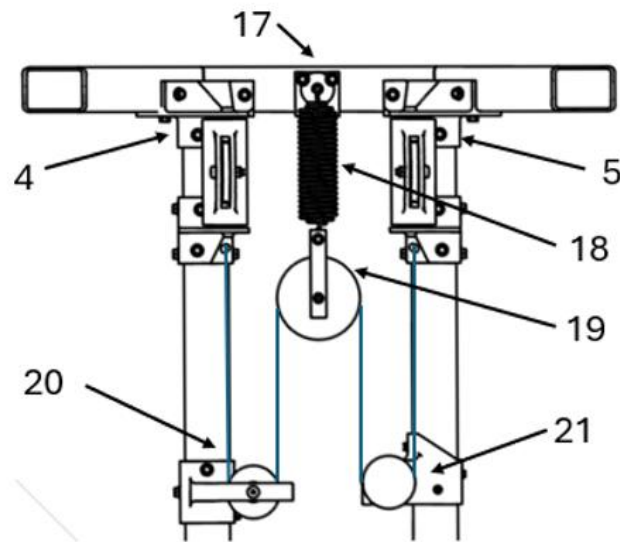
Conjunto de subensambles montados en la estructura fija.
